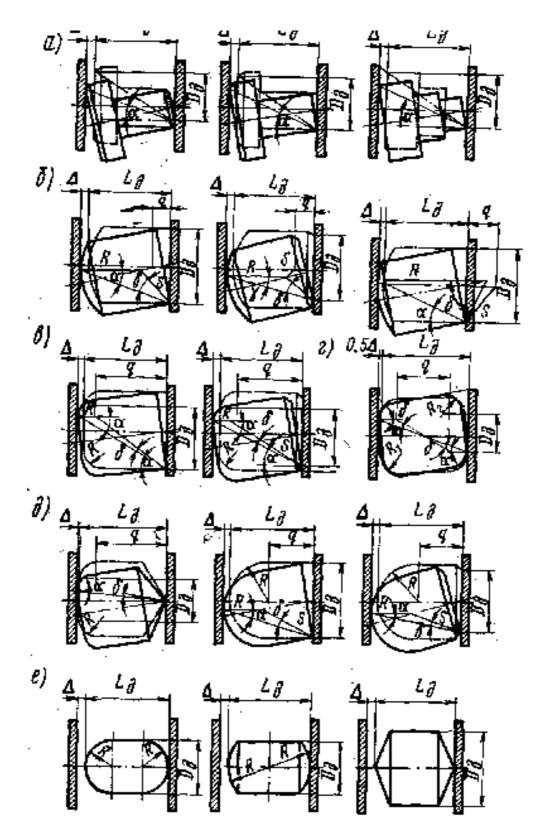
Схемы для определения зазора Δ между стенкой лотка и деталями с различной формой поверхности
